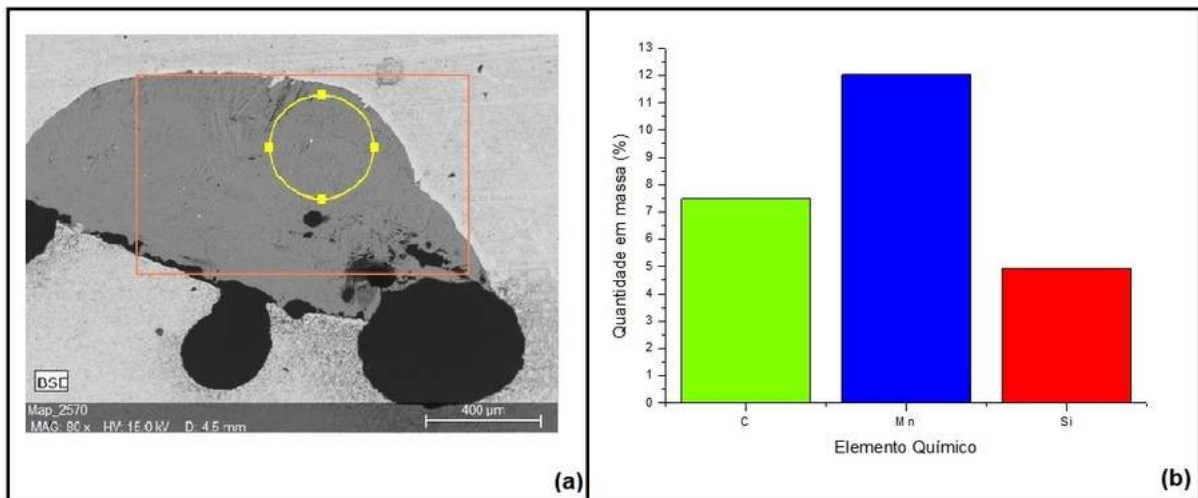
Defeito presente na zona fundida da junta soldada ST.
